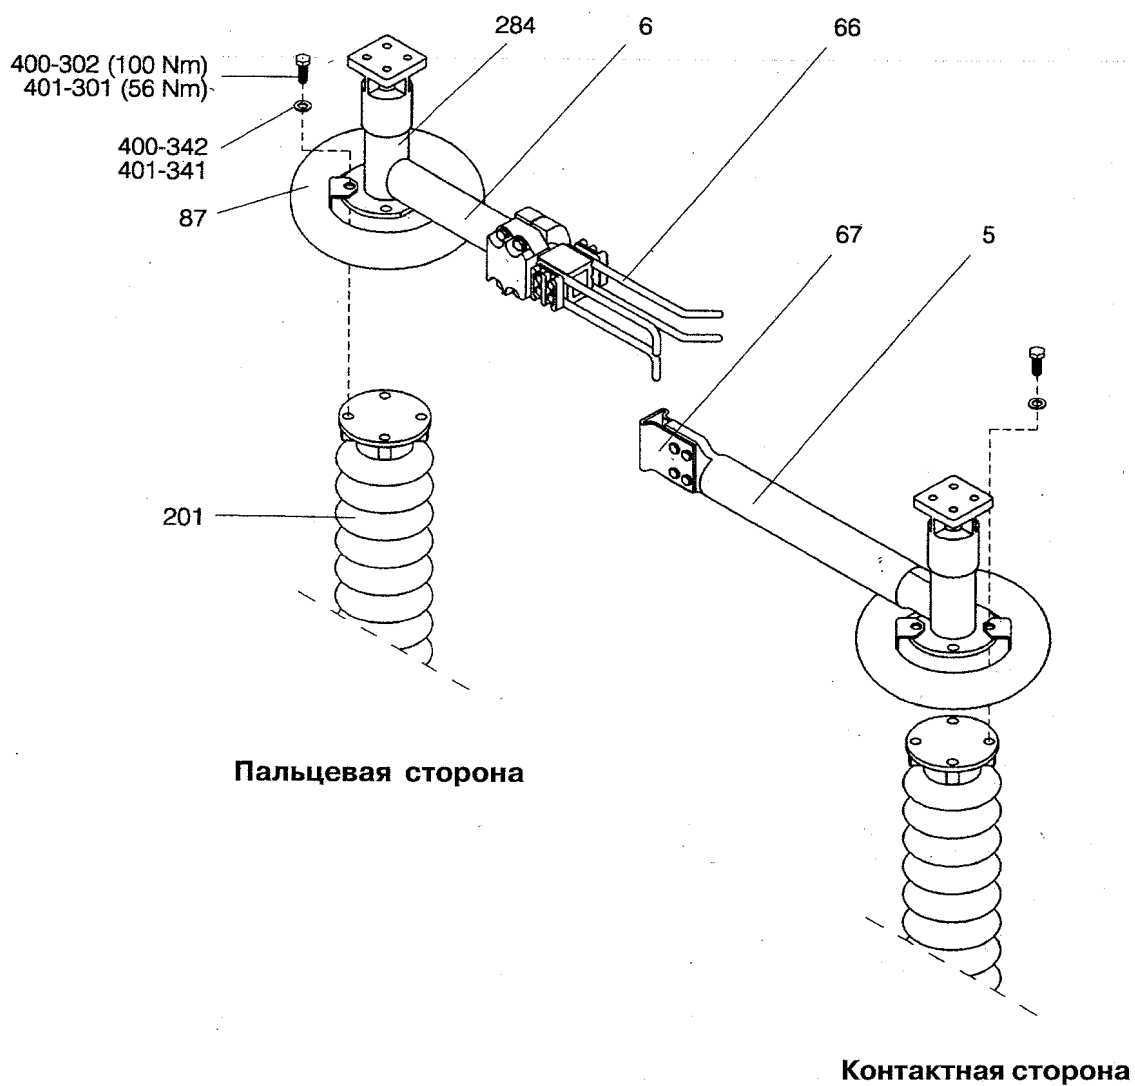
Установка разъединителя. Установка устройств защиты от короны (87) на поворотных головках (только для номинального напряжения 300 кВ)
